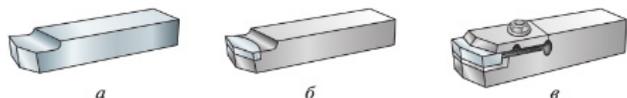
Резцы по способу крепления режущей части: а — цельный; б — с напаянной пластинкой; в — с механическим креплением пластинки
